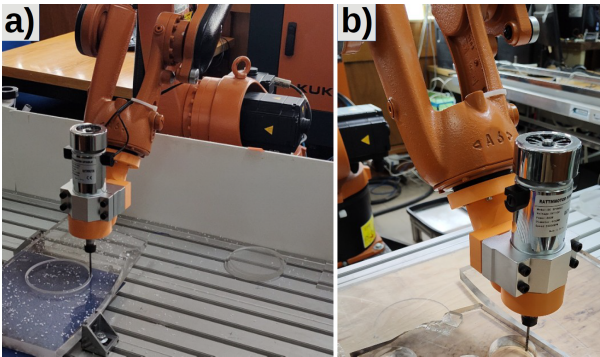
(a) Cabezal sustractivo, (b) soporte impreso en 3D ensamblado al Spindle y al brazo robótico
